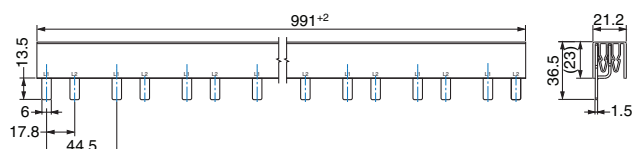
Dimensions de TMC 7...B3...CA (mm)
